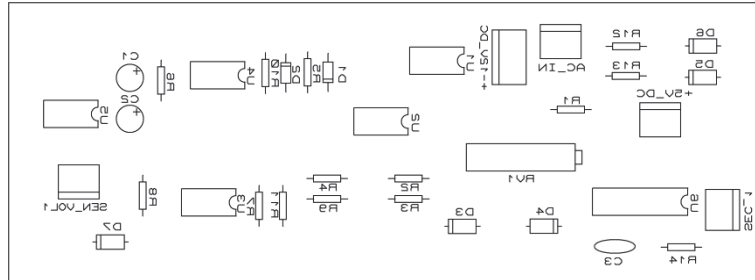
PCB del bloque de acondicionamiento de señal AC.
